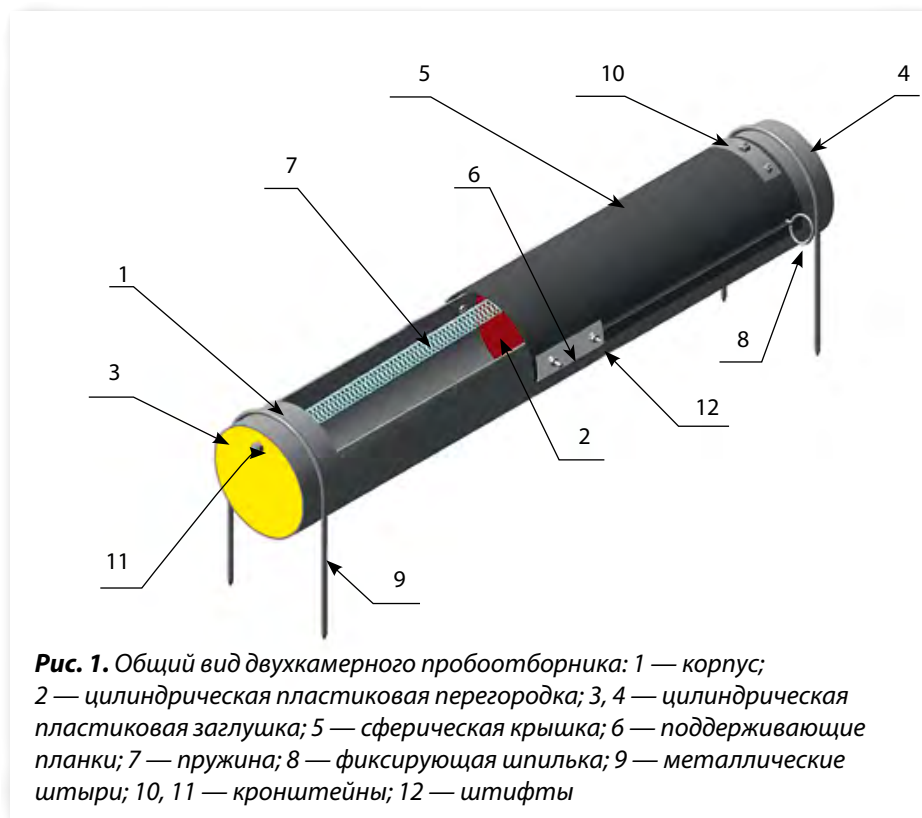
Общий вид двухкамерного пробоотборника: 1 — корпус; 2 — цилиндрическая пластиковая перегородка; 3, 4 — цилиндрическая пластиковая заглушка; 5 — сферическая крышка; 6 — поддерживающие планки; 7 — пружина; 8 — фиксирующая шпилька; 9 — металлические штыри; 10, 11 — кронштейны; 12 — штифты
